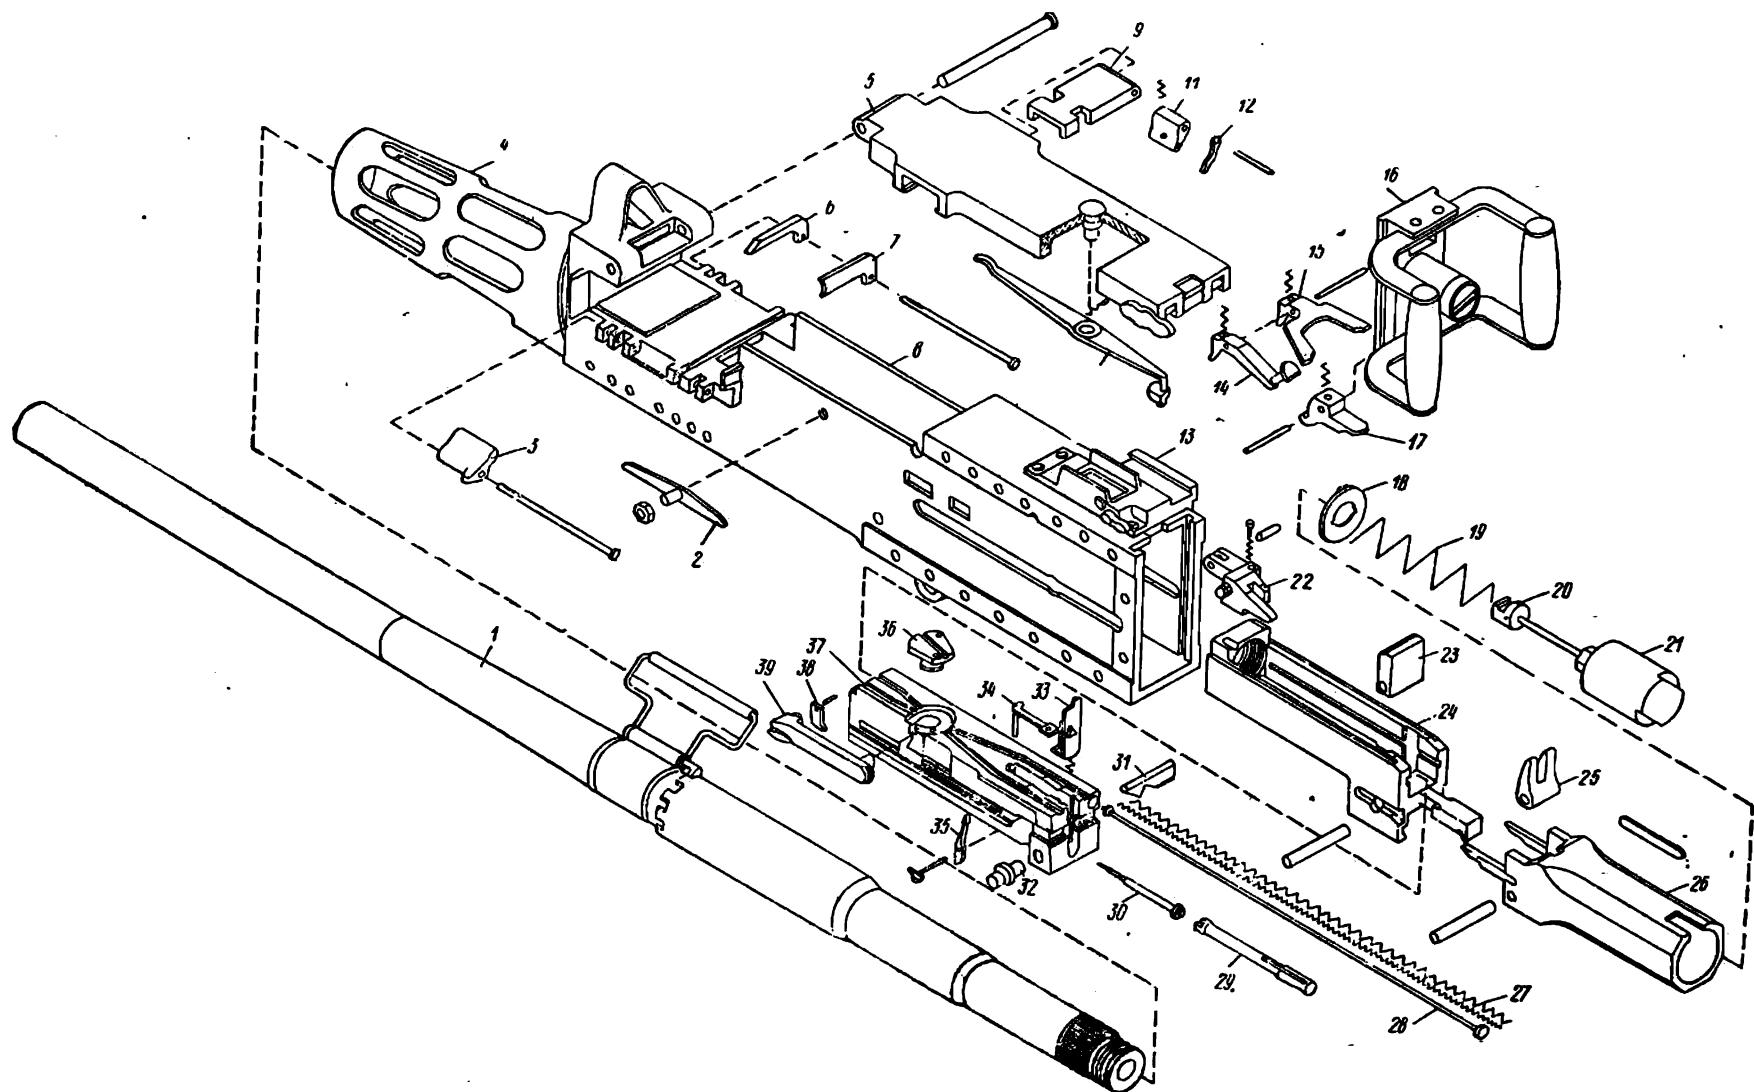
Детали и сборки пулемета Браунинга (М2НВ):
